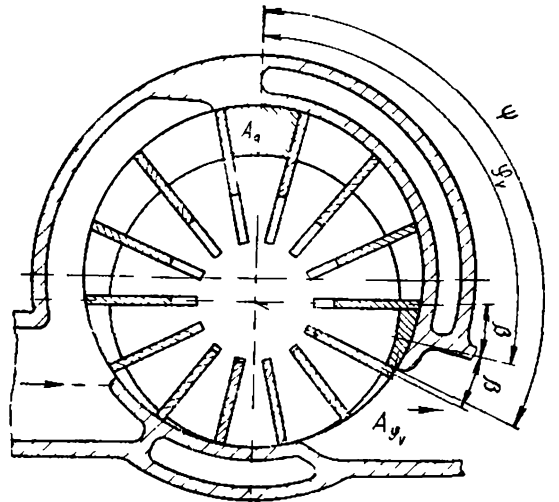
Схема к расчету угла верхней кромки нагнетательного окна ψ , определяемого степенью повышения давления
